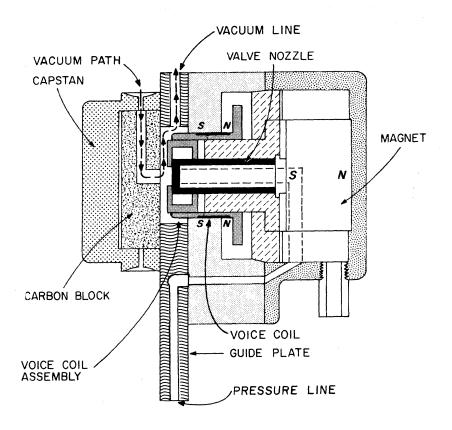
CAPSTAN-Ventil, gezeichnete Stellung Vacuum
